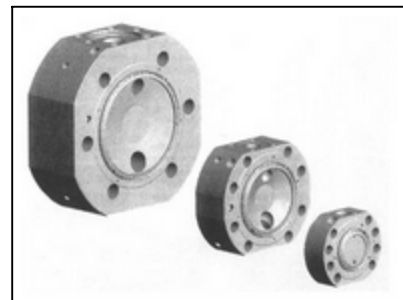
Teilefamilie „Membranpumpenkörper...“ [54]
